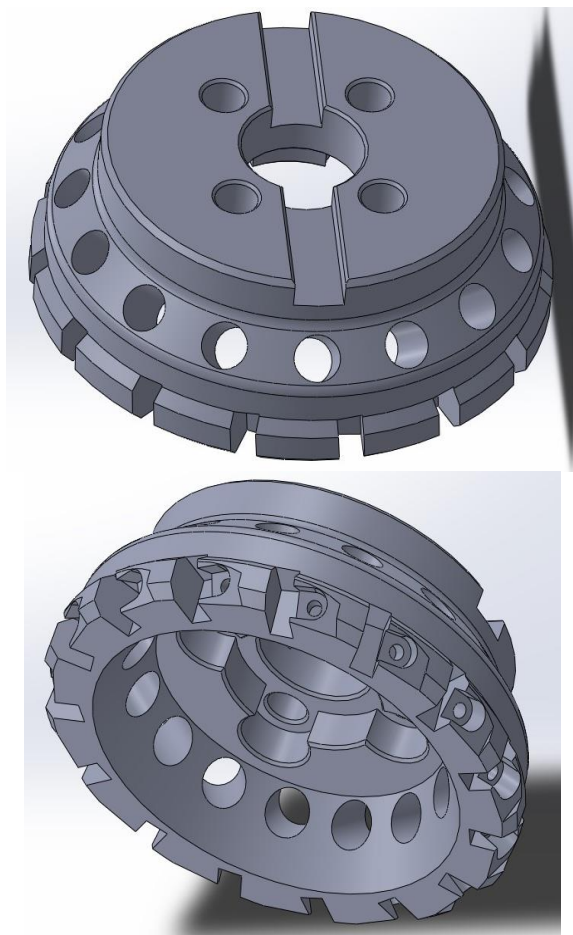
3D-модель корпуса торцевой фрезы
